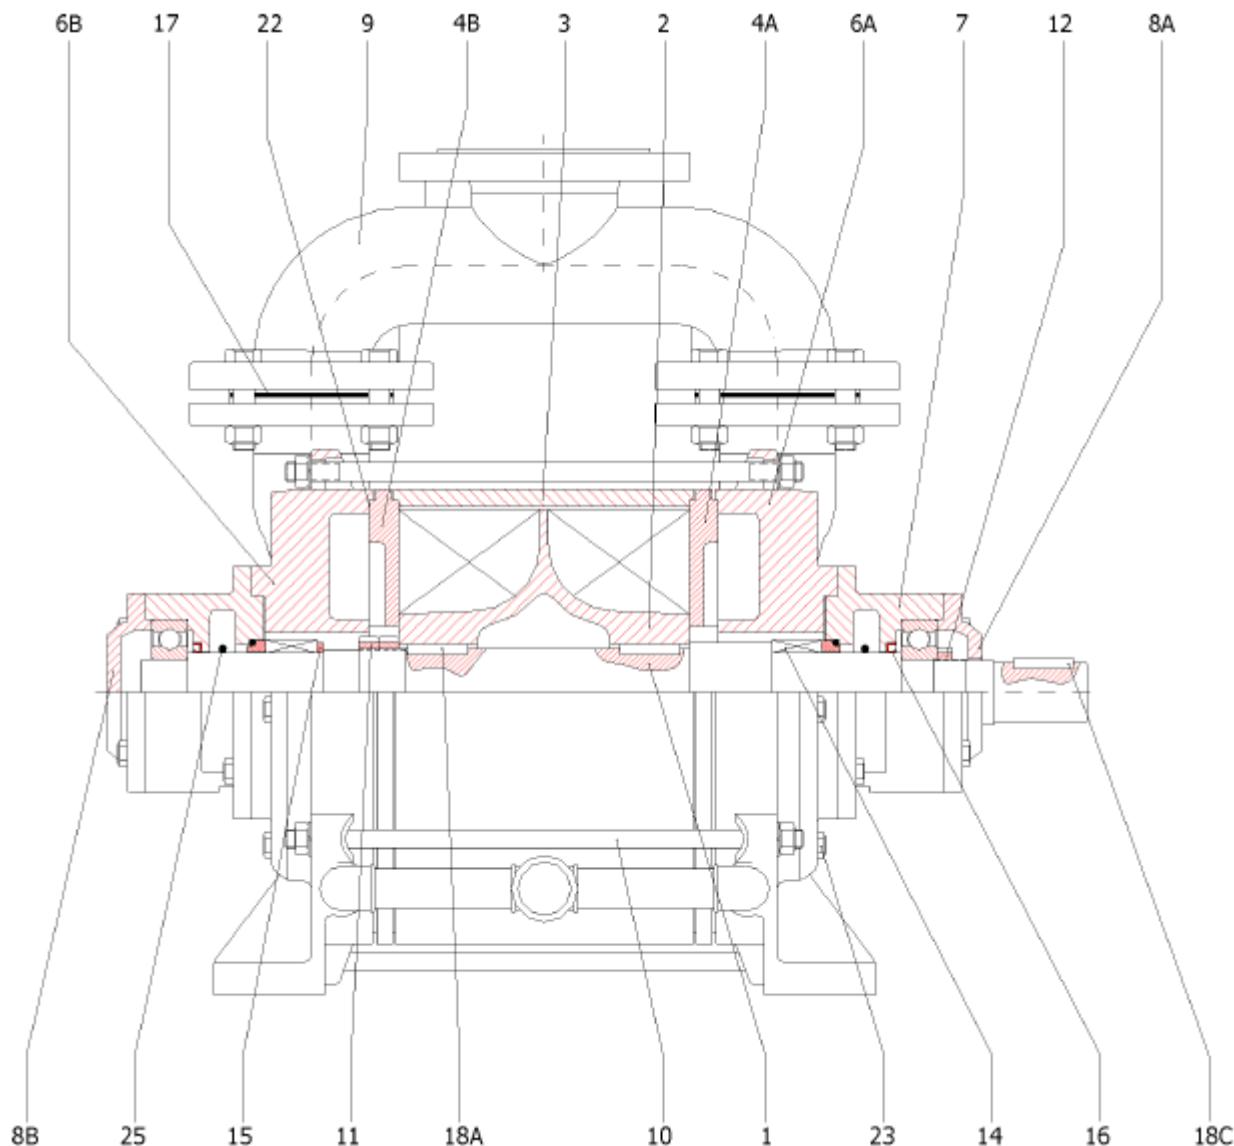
Сборочный чертеж GMVT 275, GMVT 410, GMPT 520
